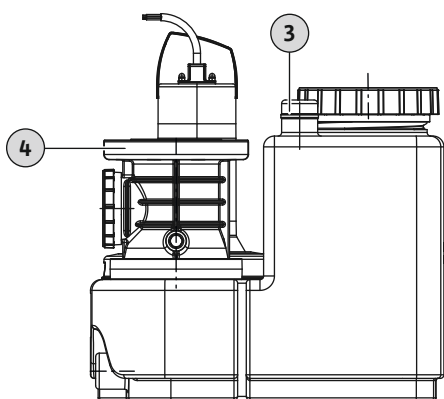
Під'єднання припливно-втяжної вентиляції до збірного резервуару
